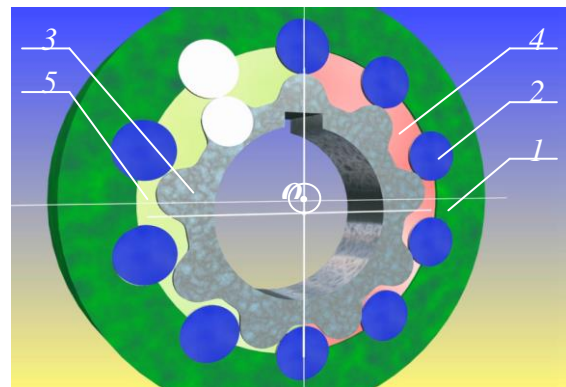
Планетарное движение вытеснителей: 1 – охватывающий вытеснитель; 2 – зубья (роликки); 3 – охватываемый вытеснитель; 4 – зона нагнетания; 5 – зона слива
